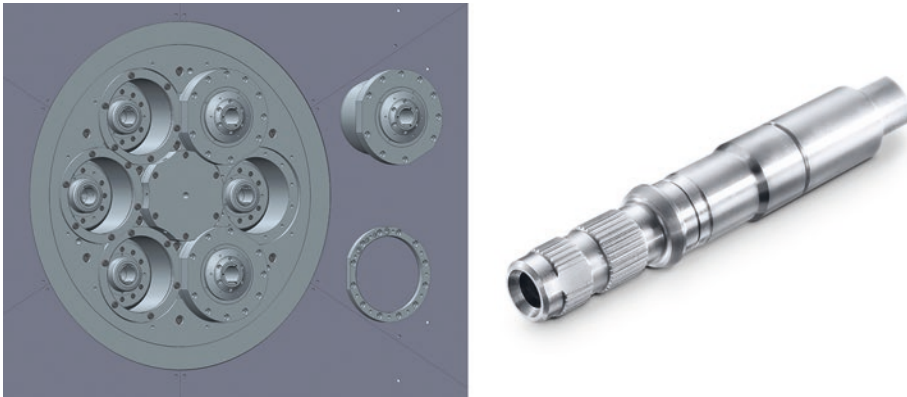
Swisstypekit als zusätzliche Führungsbuchse (links) und Gelenkwelle als typisches Werkstück (rechts) für die Bearbeitung im Langdrehverfahren [Dmgm17]
